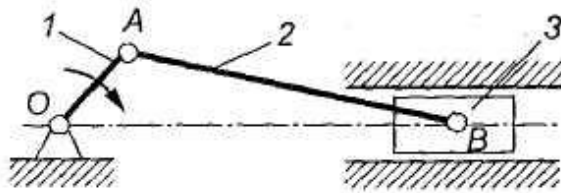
Кривошипно-шатунный механизм: 1 – кривошип; 2 – шатун; 3 – ползун
